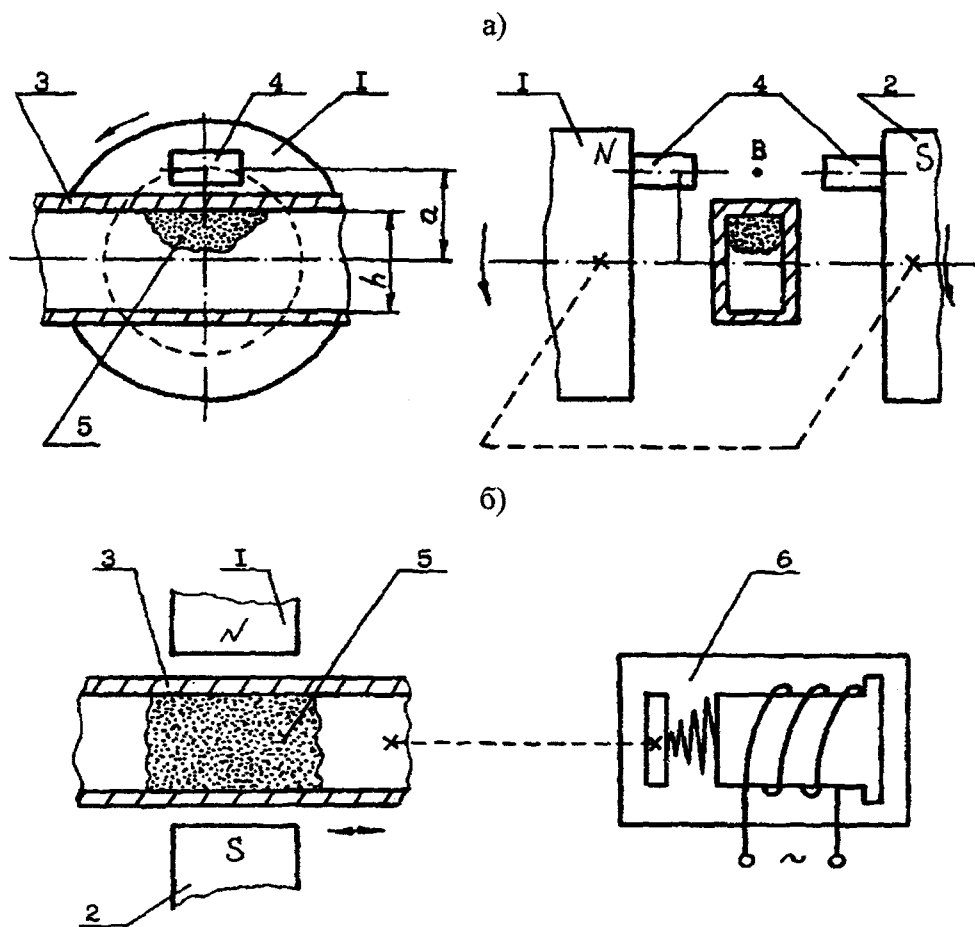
Схемы магнитно-абразивной обработки внутренней поверхности профиля без осцилляции (а) и с осцилляцией (б) образца: 1, 2 – полюсные наконечники; 3 – обрабатываемый образец; 4 – концентратор магнитного потока; 5 – ферроабразивный порошок; 6 – электромагнитный привод осцилляции
